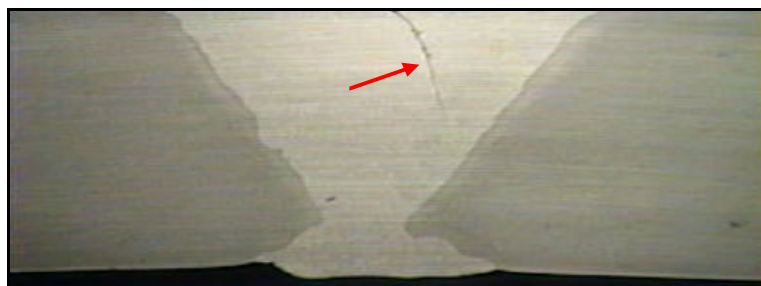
Aplicação de líquido penetrante em junta soldada evidenciando uma trinca.
